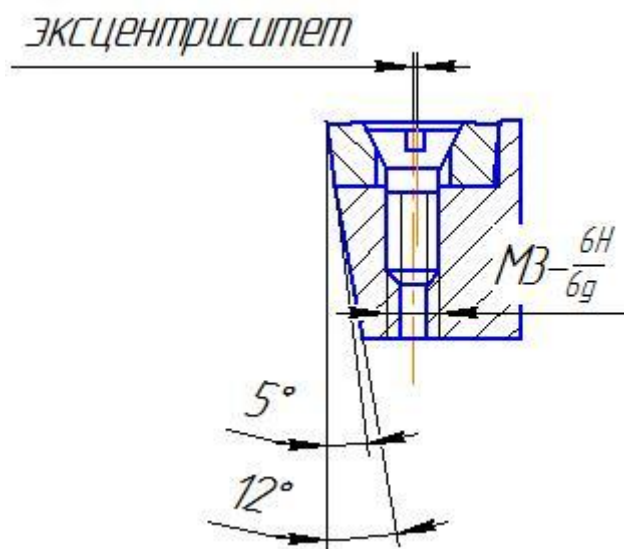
Узел крепления пластины в корпусе инструмента
